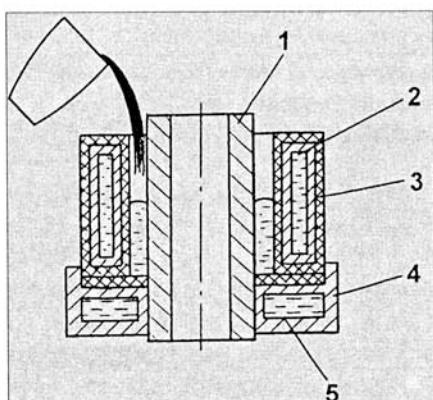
Индукционная наплавка заливкой жидкого присадочного металла на подогретый основной металл
